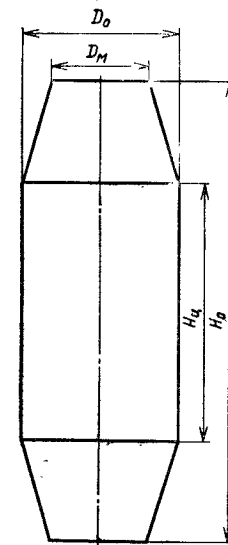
Фасонная заготовка для малооблойной штамповки шариков
